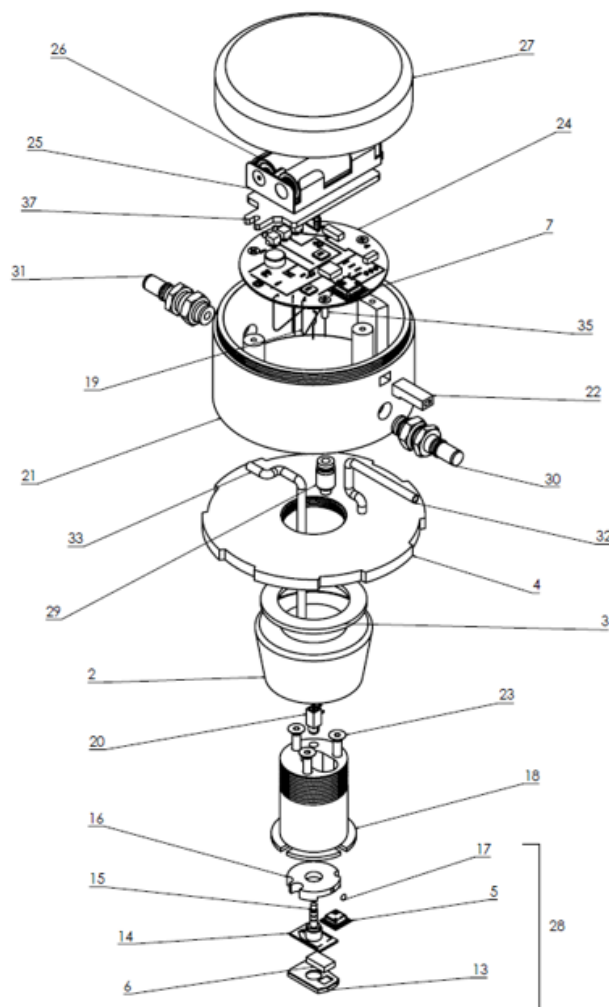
Vista explosionada del aparato según la tercera forma de realización.
